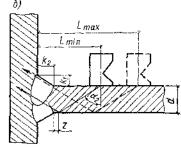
Схемы контроля тавровых сварных соединений с полным проваром
